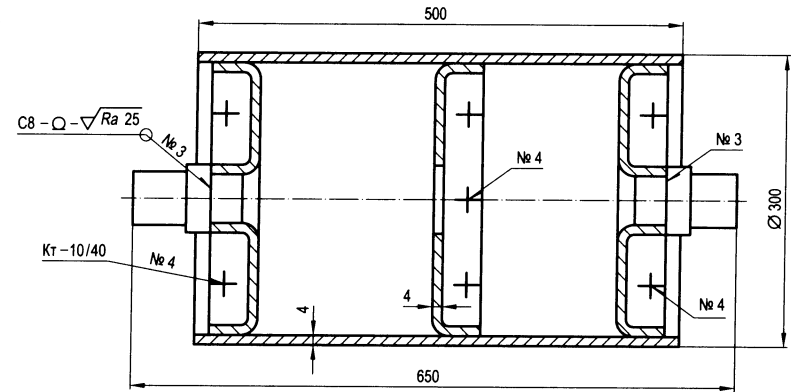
Штампо-сварной отклоняющий барабан ленточного конвейера
